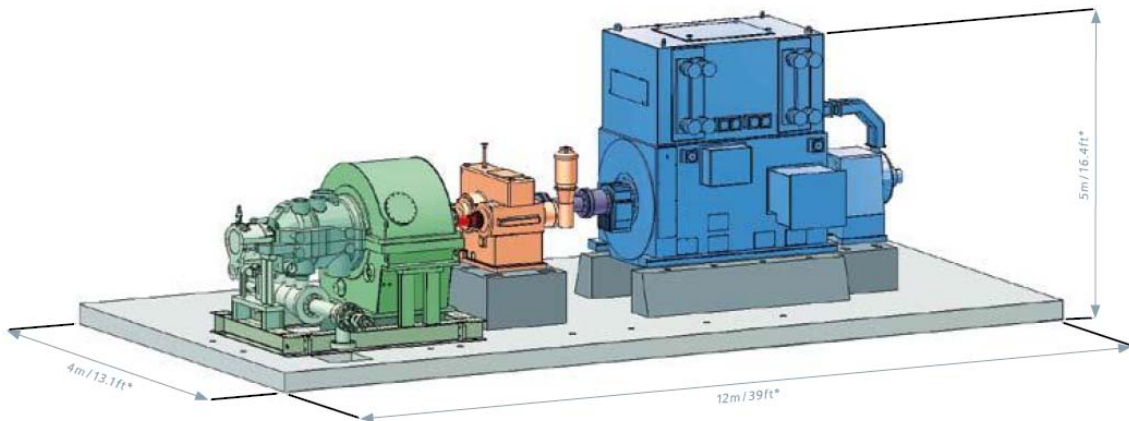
Dimensiones de la turbina de vapor SST-150 de Siemens.
